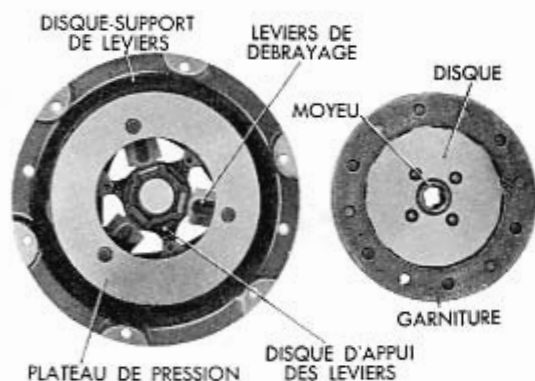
Ensemble embrayage, vu du côté plateau de pression, et disque entraîné.
